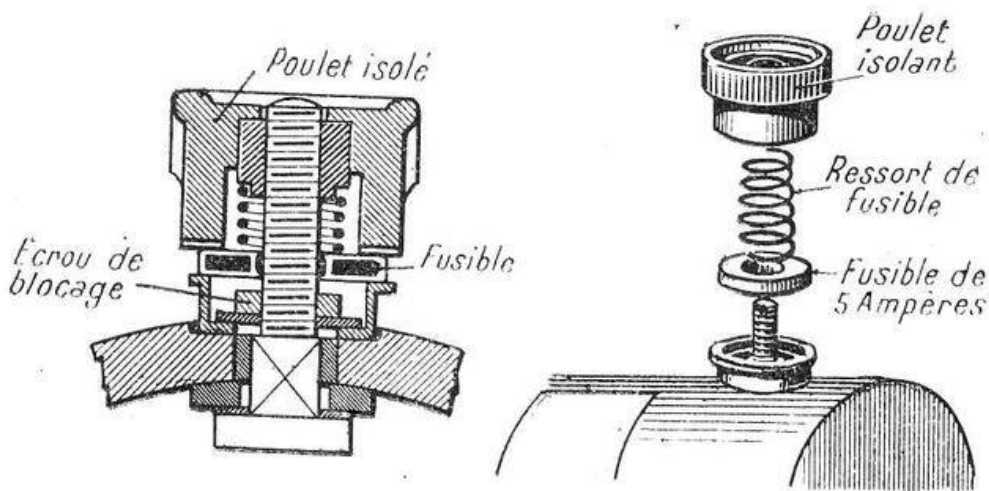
Vue en coupe et montage d'un fusible à pastille.
